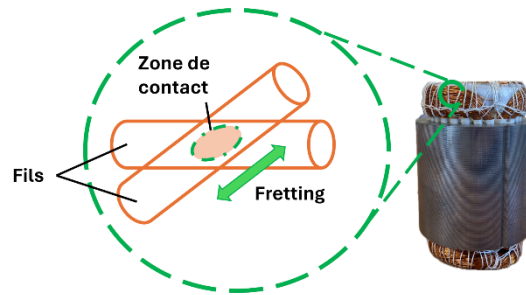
Illustration des défauts d'enroulements causant des contacts inter fils elliptiques.
